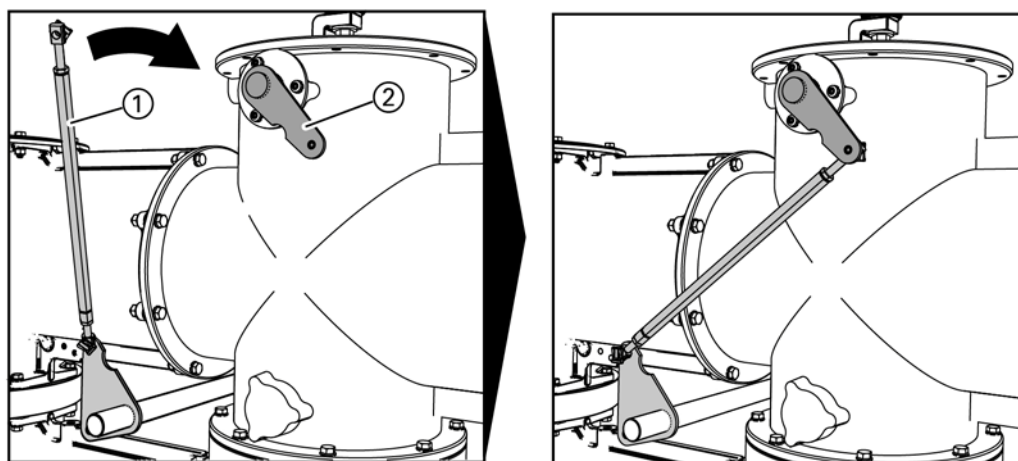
Закрепите соединительную тягу на верхнем корпусе сборных шин
